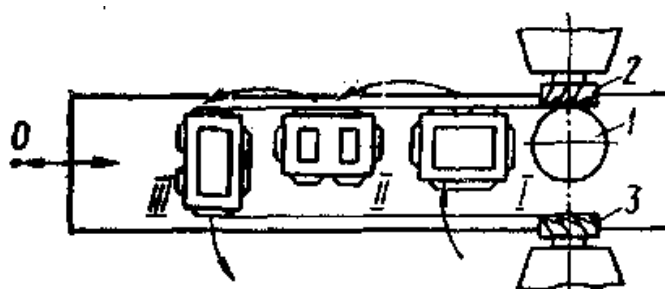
Послідовність фрезерування площин корпусної заготовки за методом «перекладання»: 1 — фреза з вертикально розташованою віссю обертання для обробки верхньої та нижньої горизонтальних поверхонь; 2,3 - фрези з горизонтально розташованими осями обертання (для обробки бічних та торцевих поверхонь)
